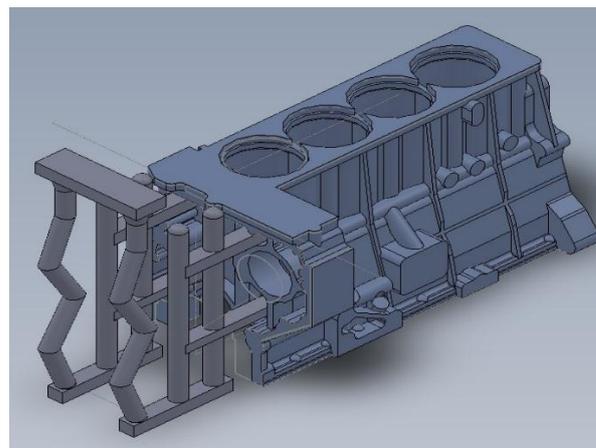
3D-модель отливки блок-картера с технологической литниково-питающей системой
